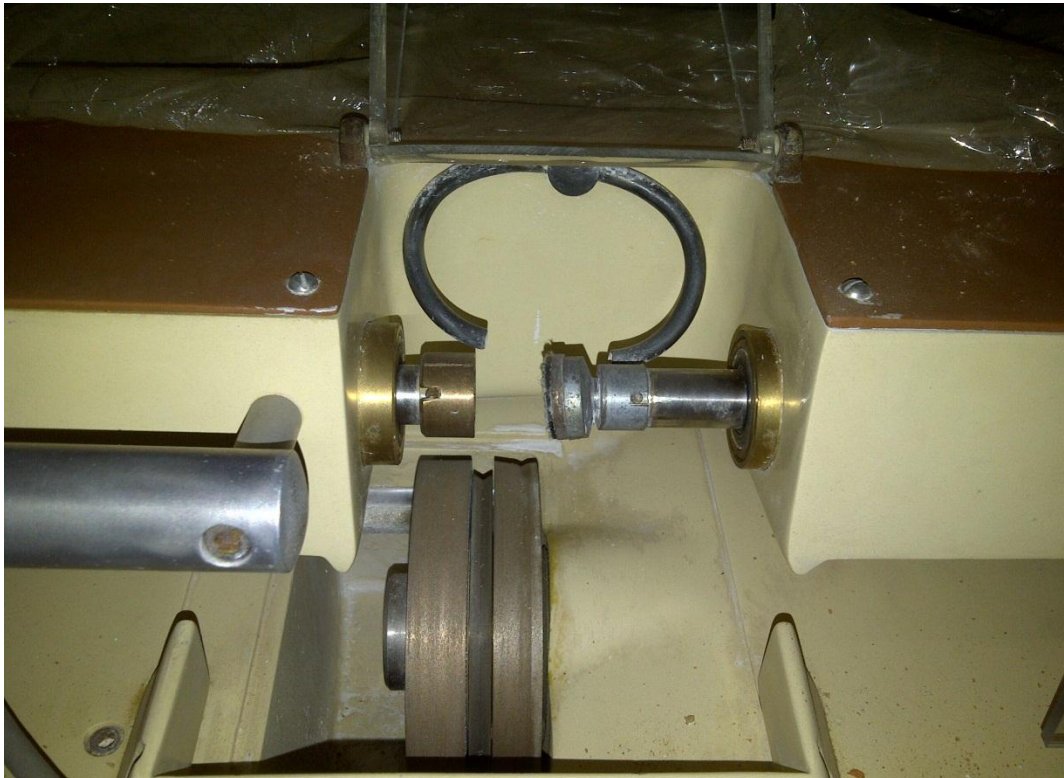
Rebolo diamantado de uma máquina de facetar.
